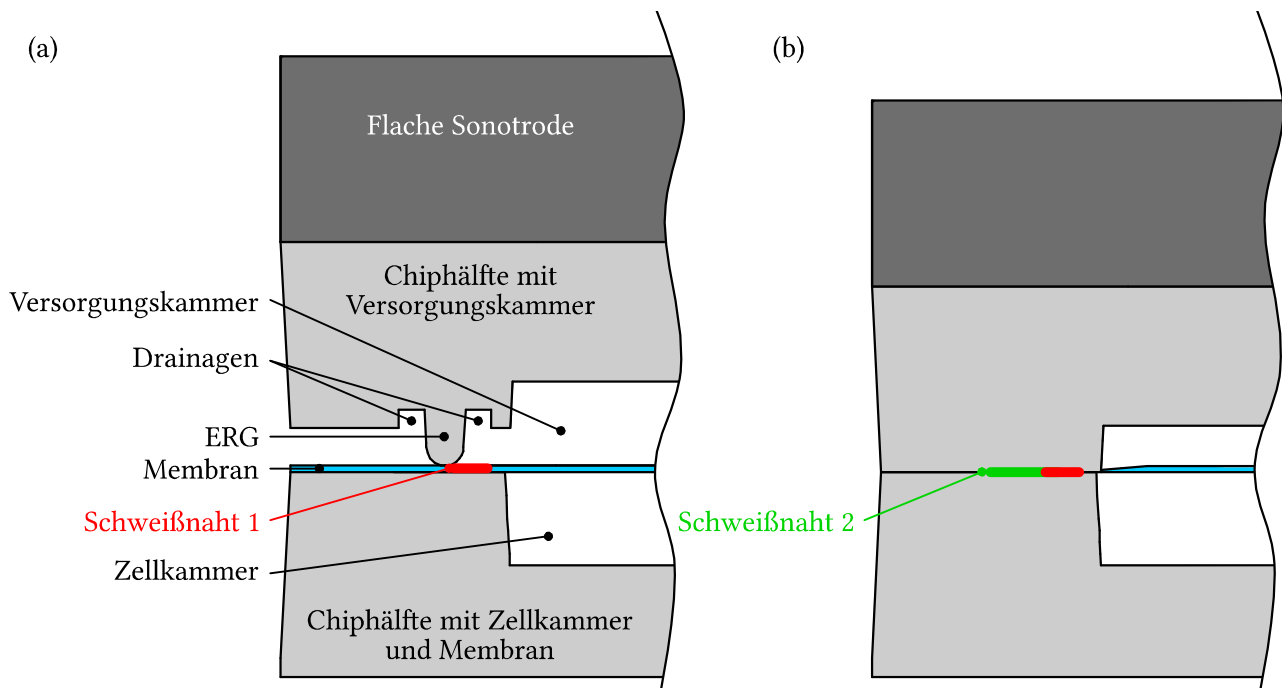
Querschnitte der zu verbindenden Komponenten (a) vor und (b) nach dem Ultraschallschweißen. Die Schweißnaht 1 aus dem ersten Schritt ist rot und die Schweißnaht 2 aus dem zweiten Schritt grün gekennzeichnet.
